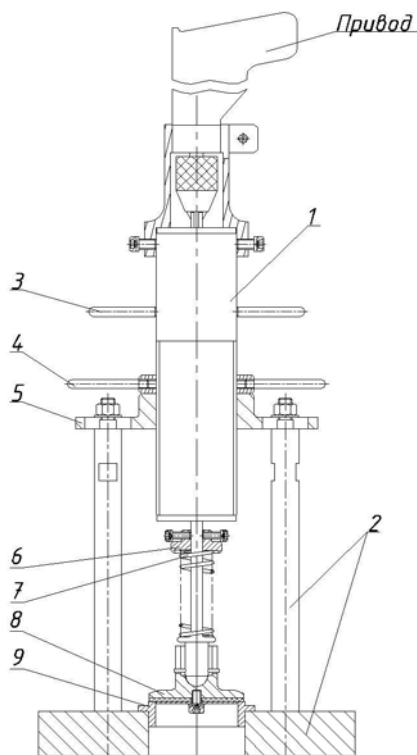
Шлифовально-притирочное устройство и стенд для отработки технологий шлифования на деталях-свидетелях: привод от электродвигателя 230V-1200W; $n_0=0 \div 650 \text{ мин}^{-1}$; 1 - шлифовально-притирочное устройство; 2 - испытательный стенд со стойками; 3 - регулировочный маховик; 4 - специальная контрольная гайка; 5 - крестовина; 6 - опора пружины; 7 - пружина; 8 - шлифовальный блок; 9 - деталь-свидетель «седло».
